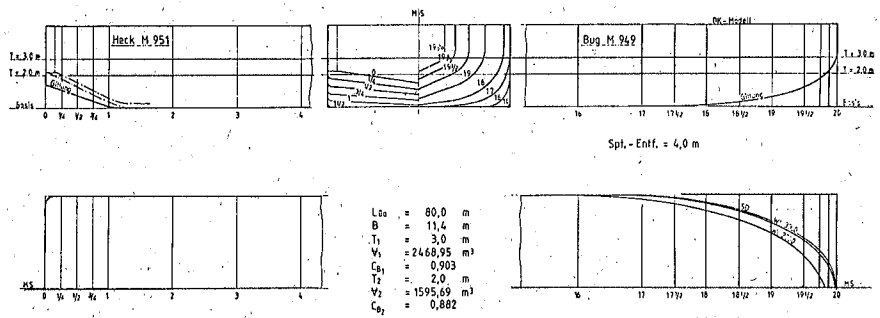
Motorgüterschiff „SEE I“, 2-Schrauber, Ellipsenbug
